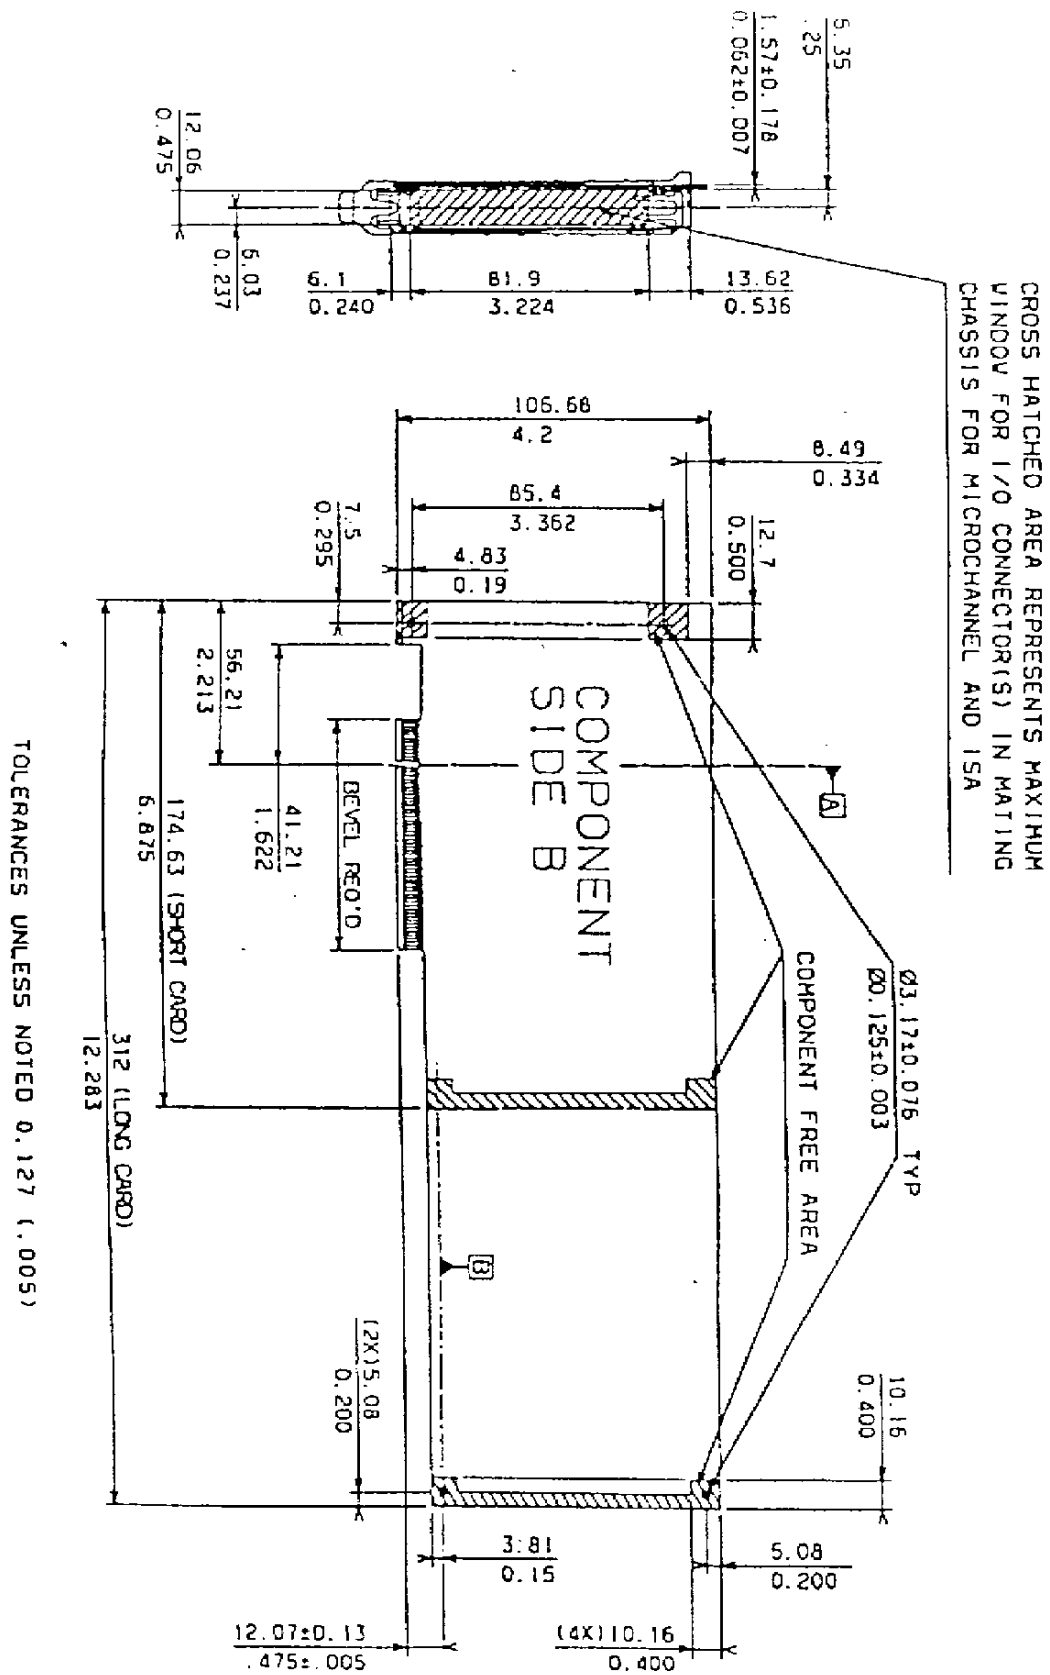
Заготовка PCI - платы (3.3В)
